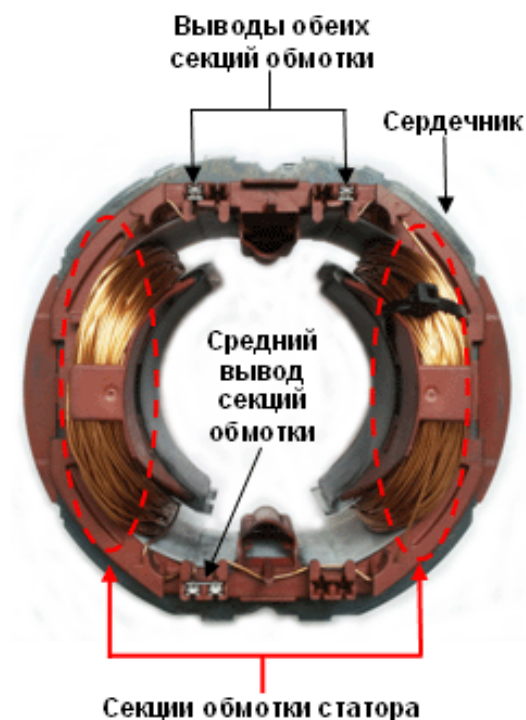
Статор коллекторного двигателя (вид с торца)
